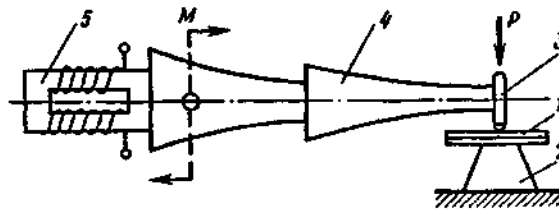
Ультразвуковая сварка: 1 – свариваемые детали; 2 – опора; 3 – наконечник; 4 – волновод; 5 – магнитострикционный преобразователь
